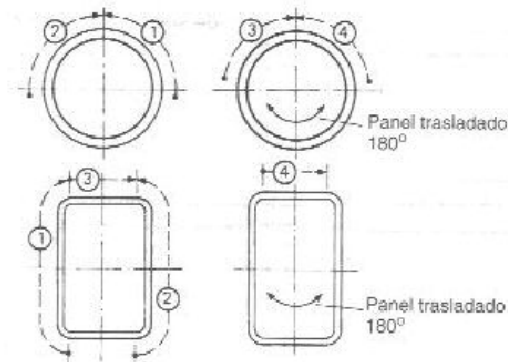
Soldadura vertical ascendente de 180°
